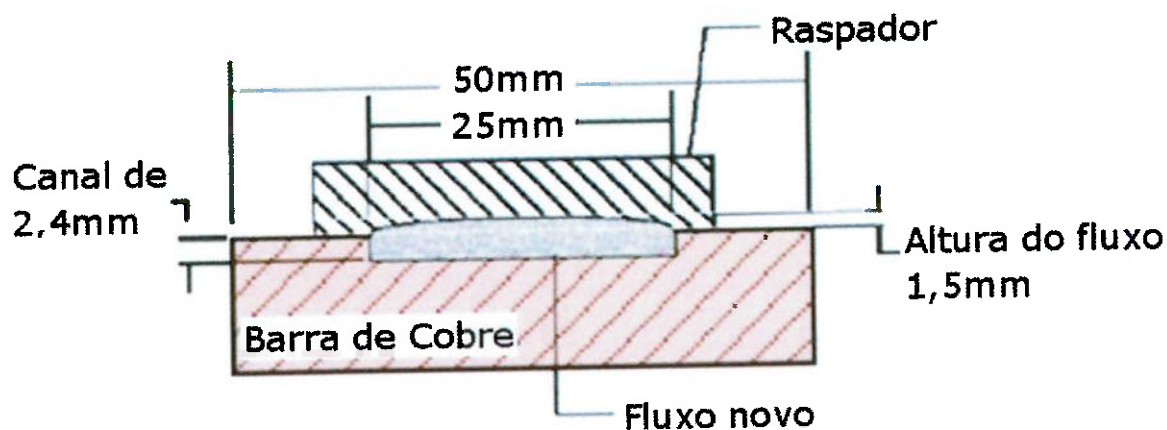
Dimensões do cobre junta utilizado na soldagem dos corpos de prova.
